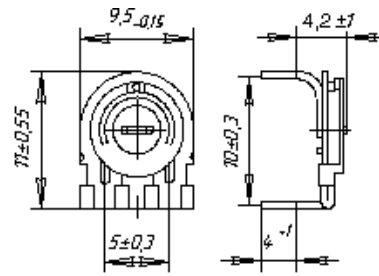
Габаритні розміри резистора типу СПЗ-386
